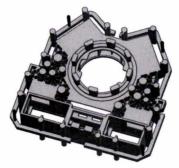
调整后的基座铸件三维浇冒系统 Fig.7 3-dimensional gating and risering system of base casting after adjustment
